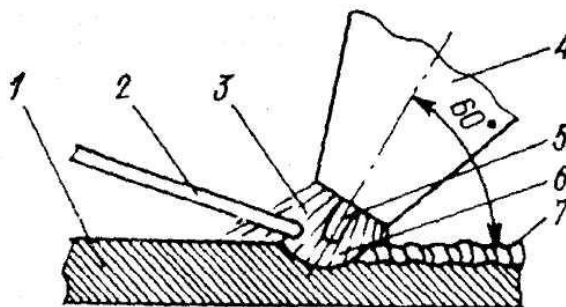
Схема аргонно-дуговой сварки неплавящимся электродом:
